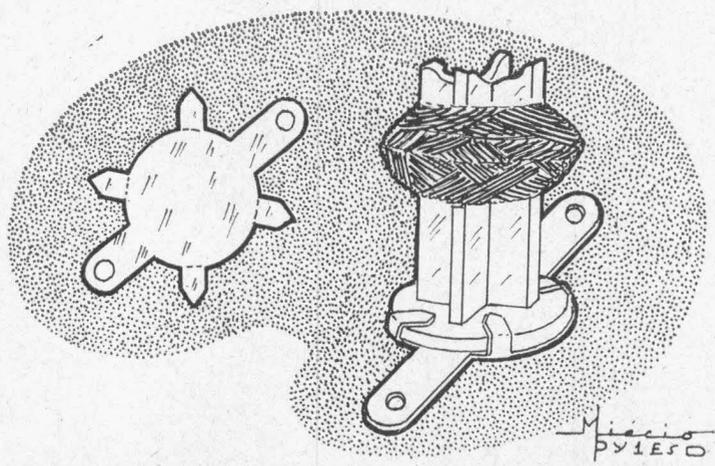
Detalhe mostrando como deve ser confeccionado o suporte para fixação do reator ao chassi.
